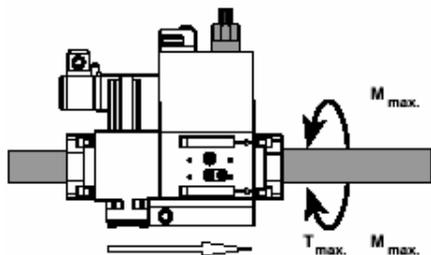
мультиблок не использовать в качестве рычага для закручивания
